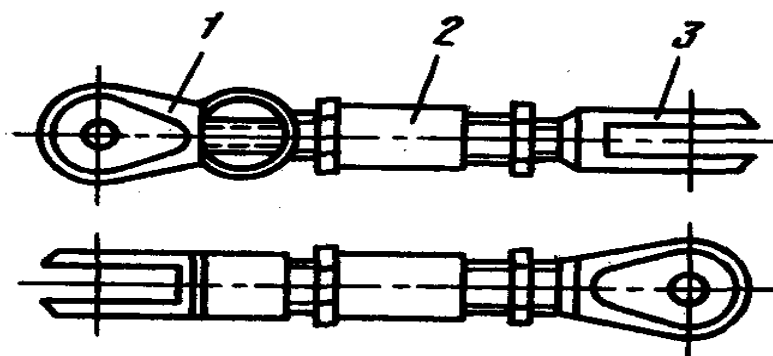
Короткая стальная нерегулируемая сварная тяга
